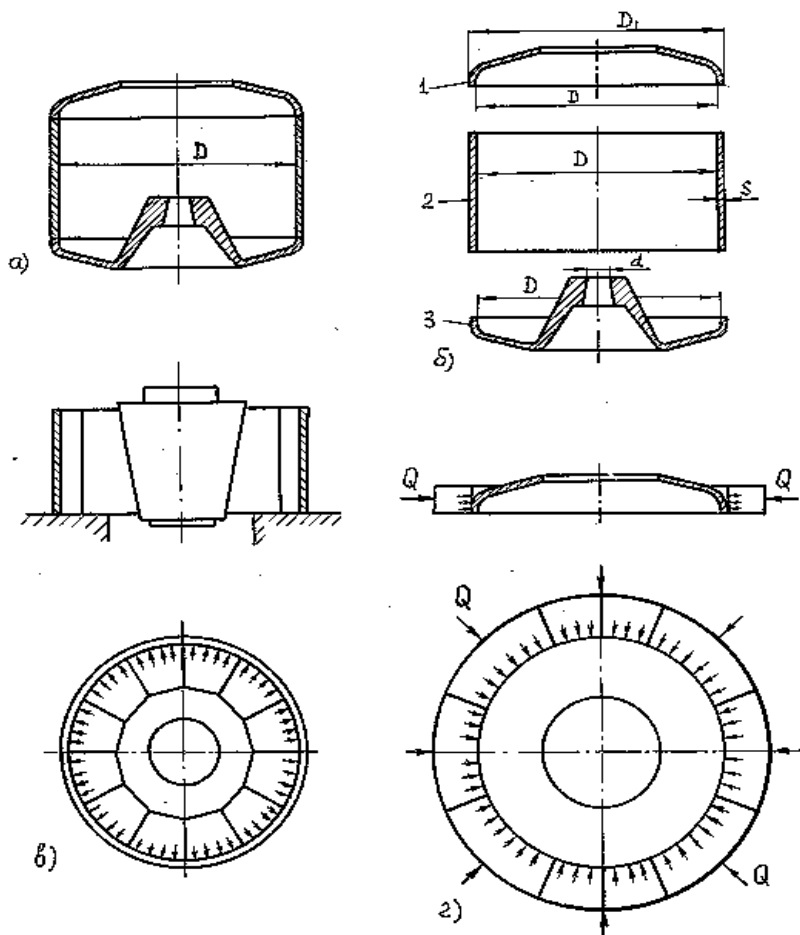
Ротор центрифуги типа ФМБ из пластически калиброванных и упрочненных элементов, схема сборки и схемы пластической калибровки:
